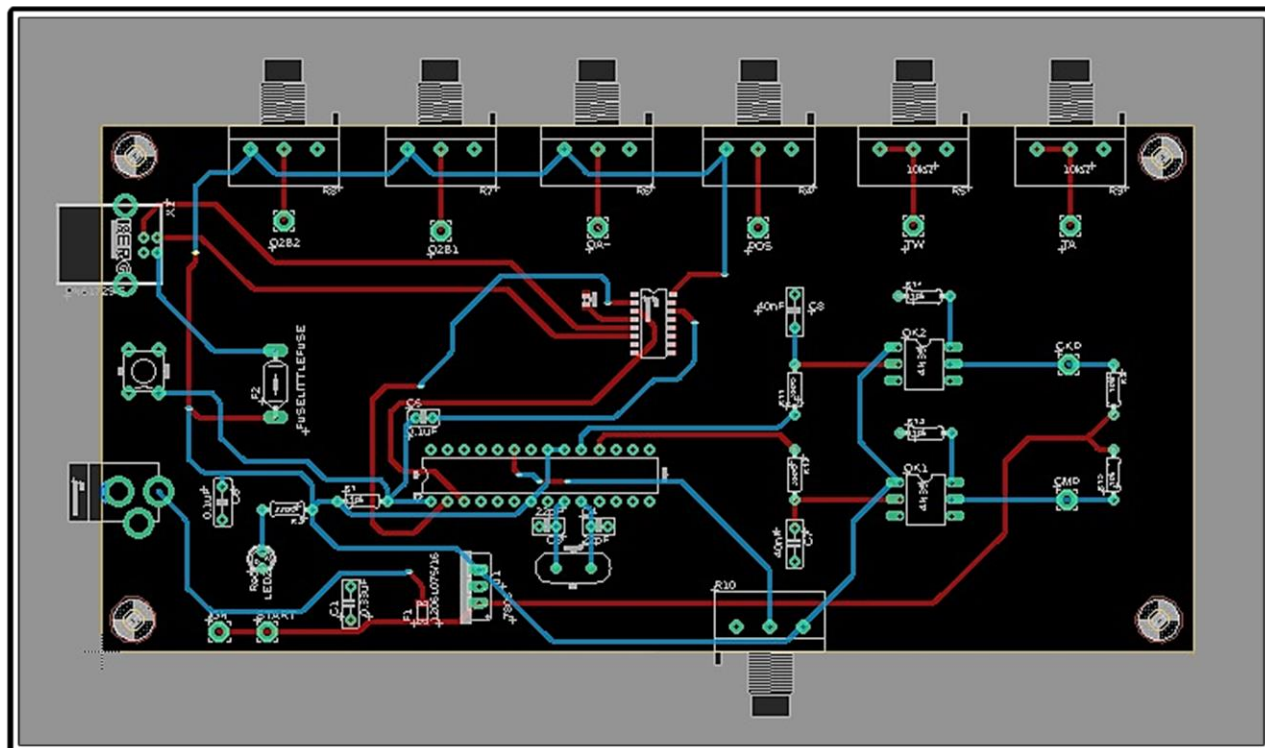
Diseño y ubicación de componentes de la placa PCB.
